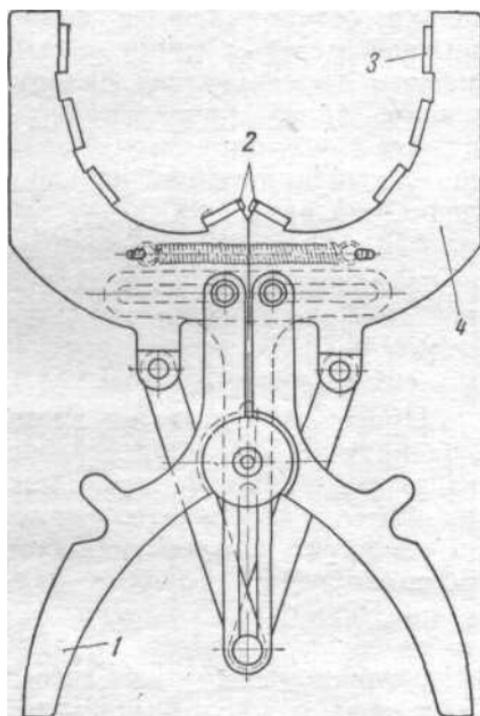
Приспособление для снятия и надевания поршневых колец на поршень
